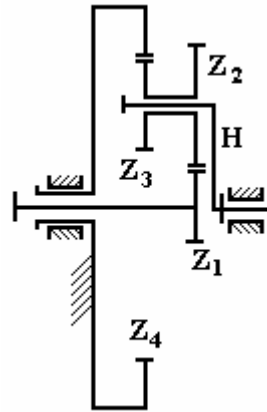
Планетарный механизм с двухрядным расположением зубчатых колес
